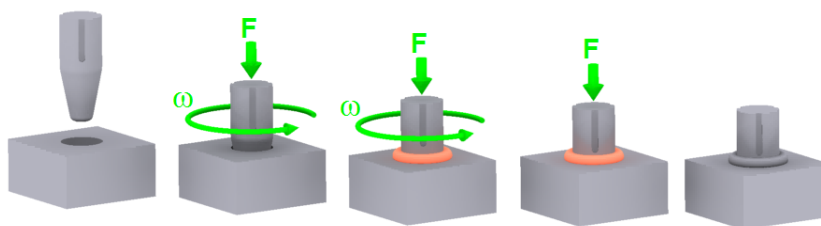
Croqui do processo de soldagem por atrito FTPW (Freitas, 2014)
